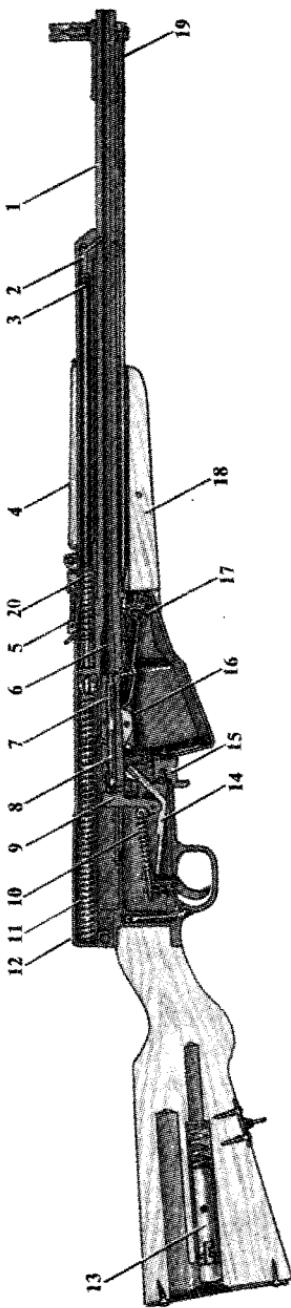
Схема карабина СКС: 1 — ствол; 2 — газовое отверстие; 3 — шток с газовыми поршнями; 4 — ствольная накладка; 5 — прицел; 6 — патронник; 7 — затвор; 8 — ударник; 9 — курок; 10 — боевая пружина; 11 — возвратный механизм с возвратной пружиной; 12 — корпус; 13 — пенал для чистки оружия; 14 — пружина спускового крючка; 15 — защелка магазина; 16 — подаватель; 17 — пружина подавателя; 18 — ложа; 19 — шомпол; 20 — толкателем с пружиной.
